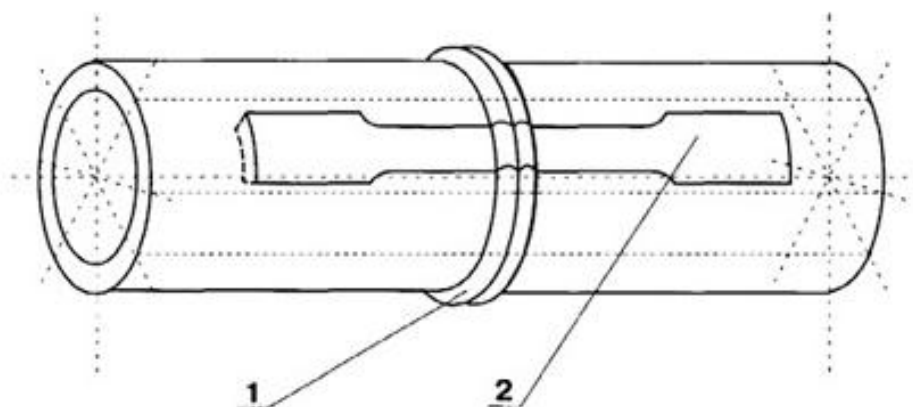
Схема вырезки образцов из контрольного соединения
